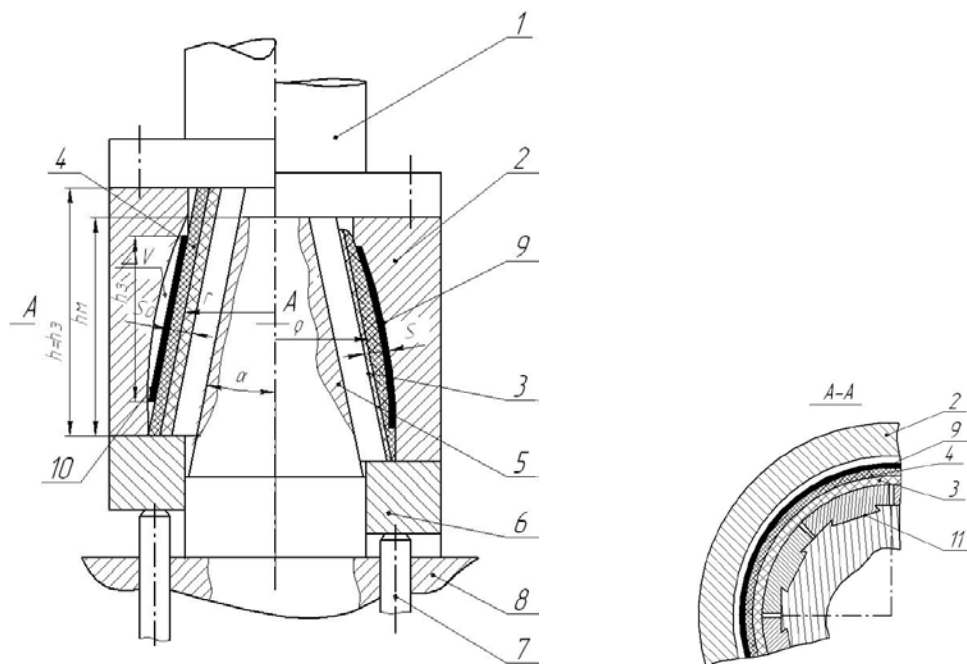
Устройство для формообразования тонкостенных осесимметричных деталей усеченной сужающейся формы:
